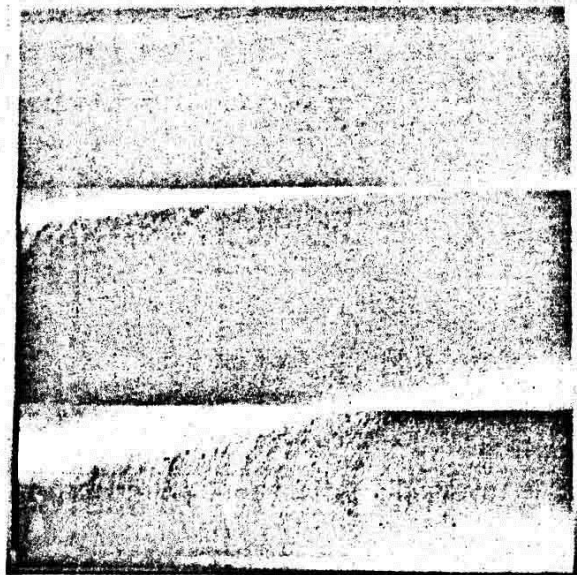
Плоская поверхность, полученная трех-проходным торцовым фрезерованием.
